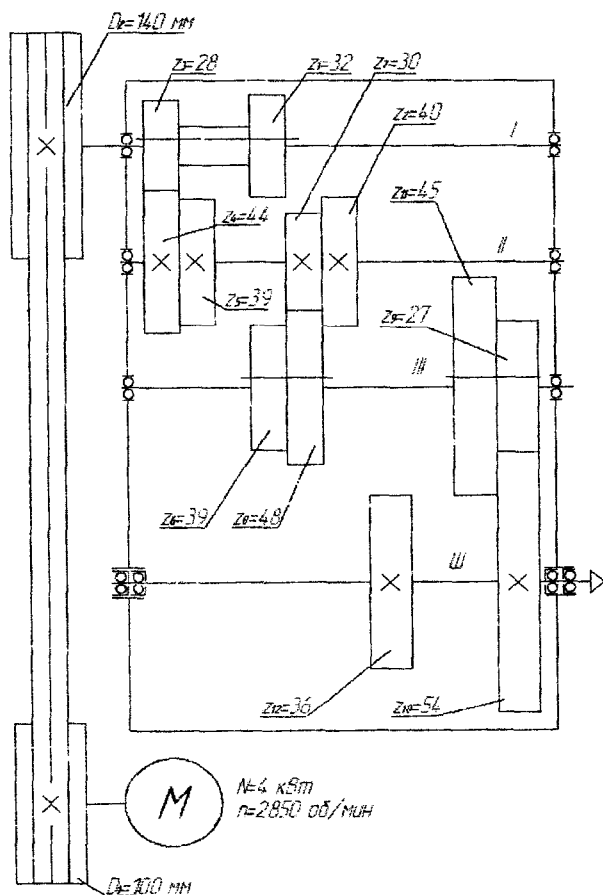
Кинематическая схема главного привода токарно-револьверного станка
